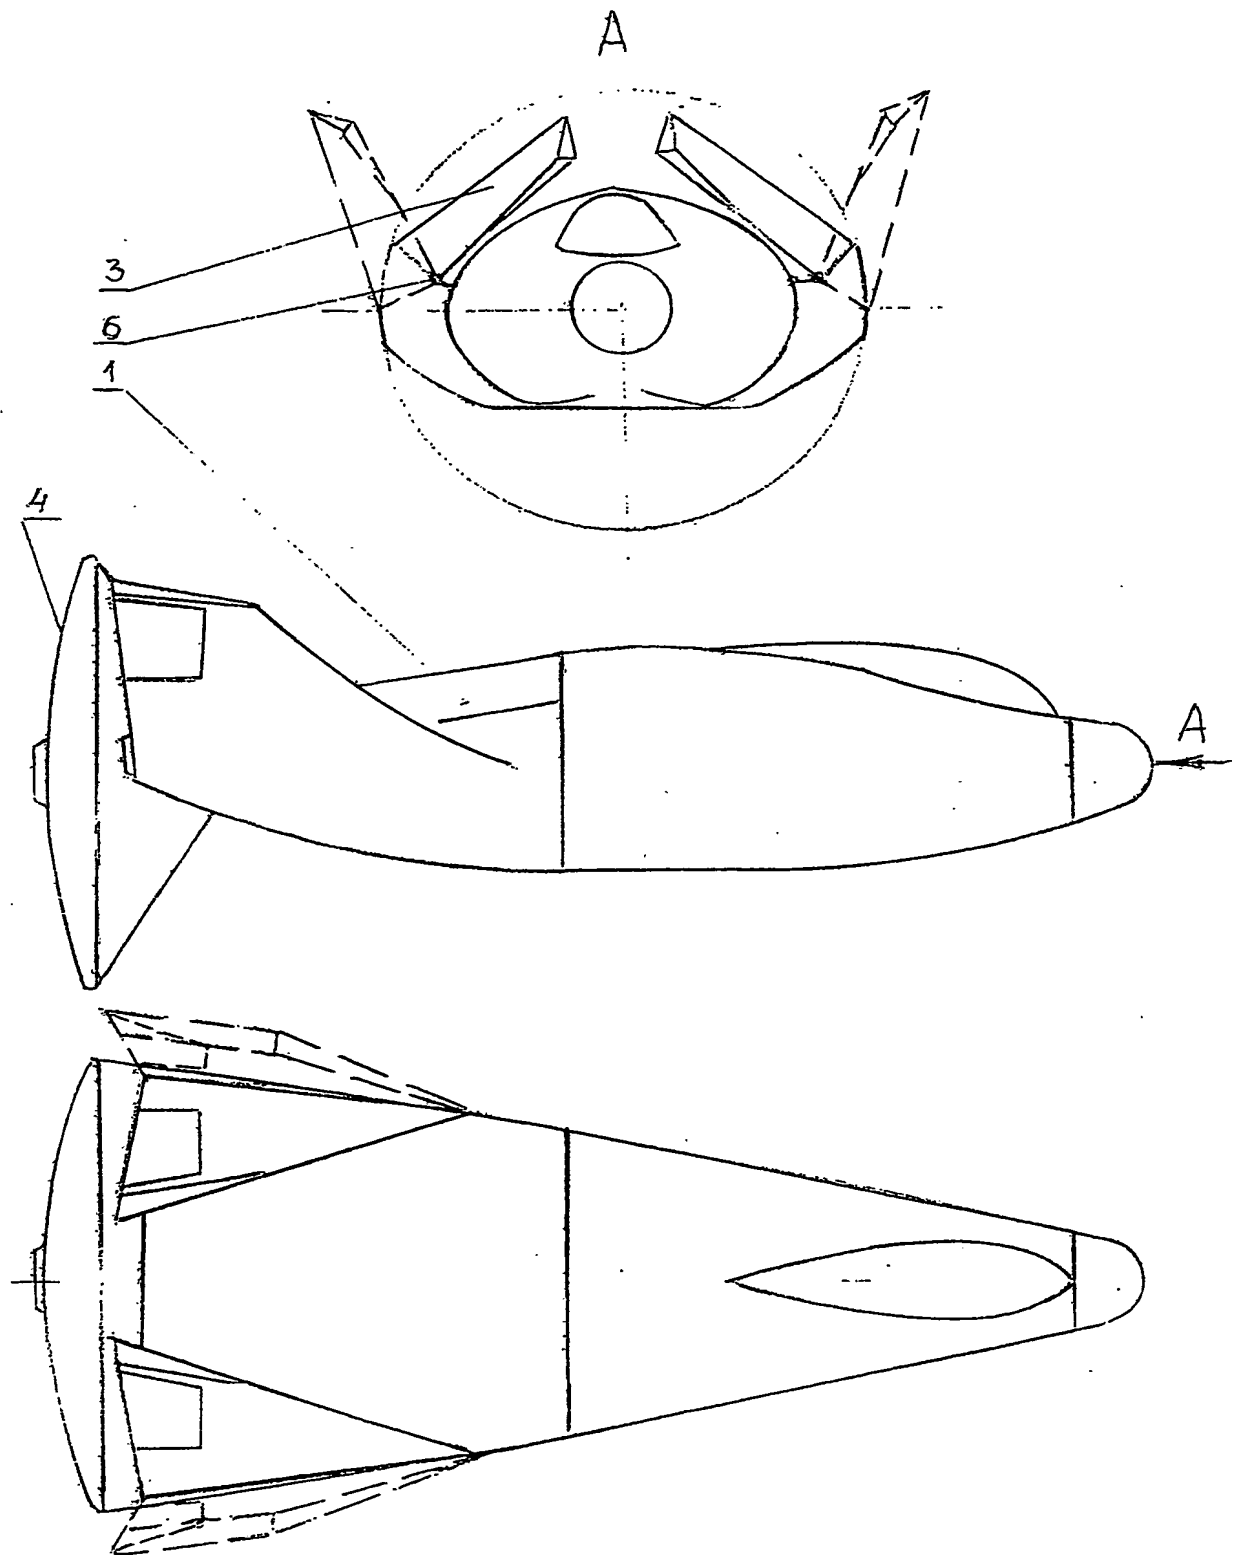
КА типа несущий корпус с разворачивающимися крыльями
